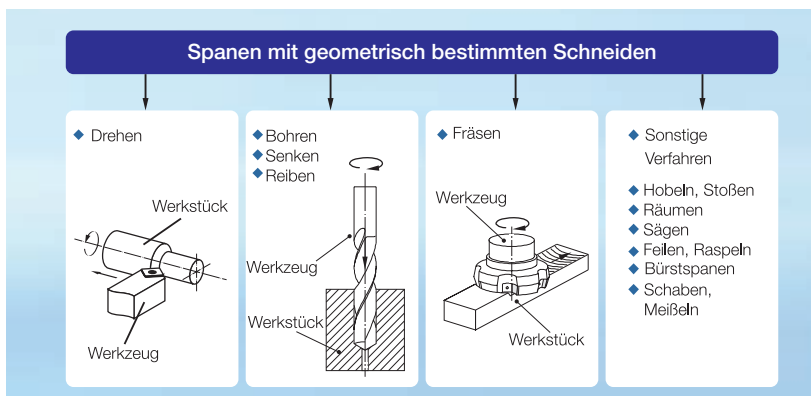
Erster Schritt der Endfertigung: Mechanische Bearbeitung bei weichem Werkstoffzustand
